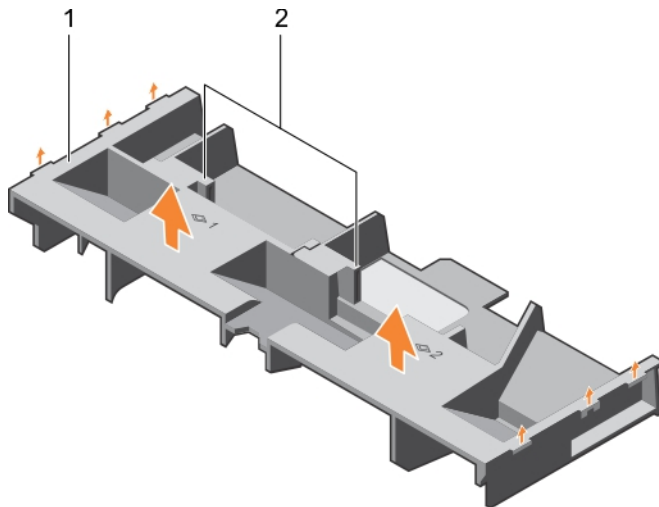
Entfernen und Einsetzen des Kühlgehäuses
